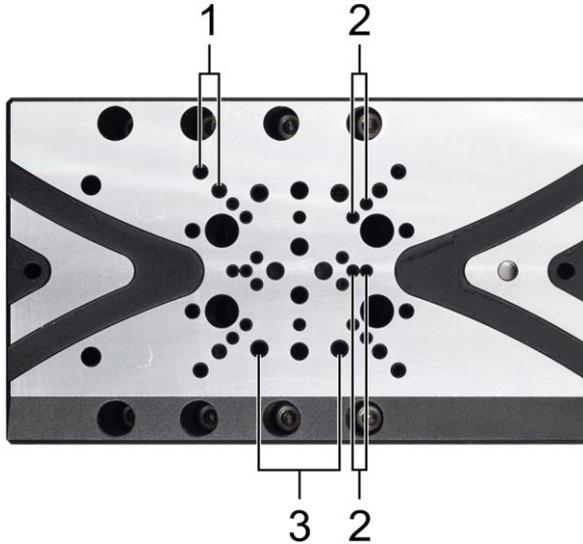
Montagebohrungen zum Befestigen der Last auf der bewegten Plattform
